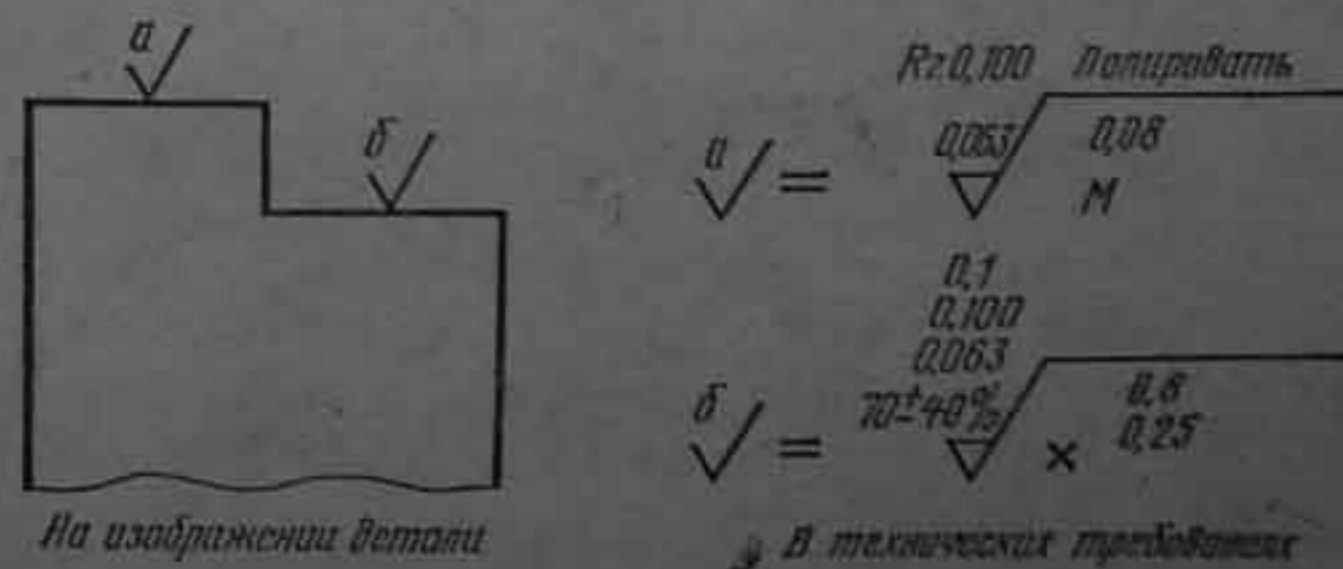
Примеры упрощенного обозначения шероховатости поверхности на чертежах
